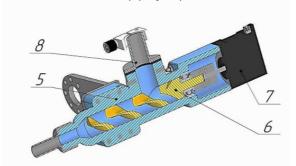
Устройство для 3D-печати строительными смесями на основе вяжущих: 5 – корпус, 6 – шнек-дозатор, 7 – шаговый двигатель, 8 – штуцер.
